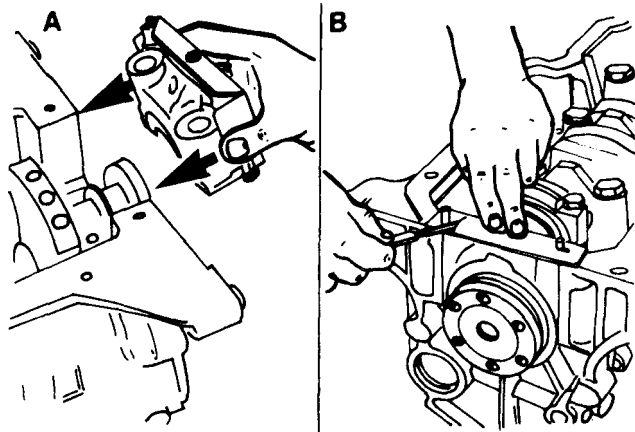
При установке упорных полуколец коленвала их бронзовая поверхность должна быть обращена наружу.
